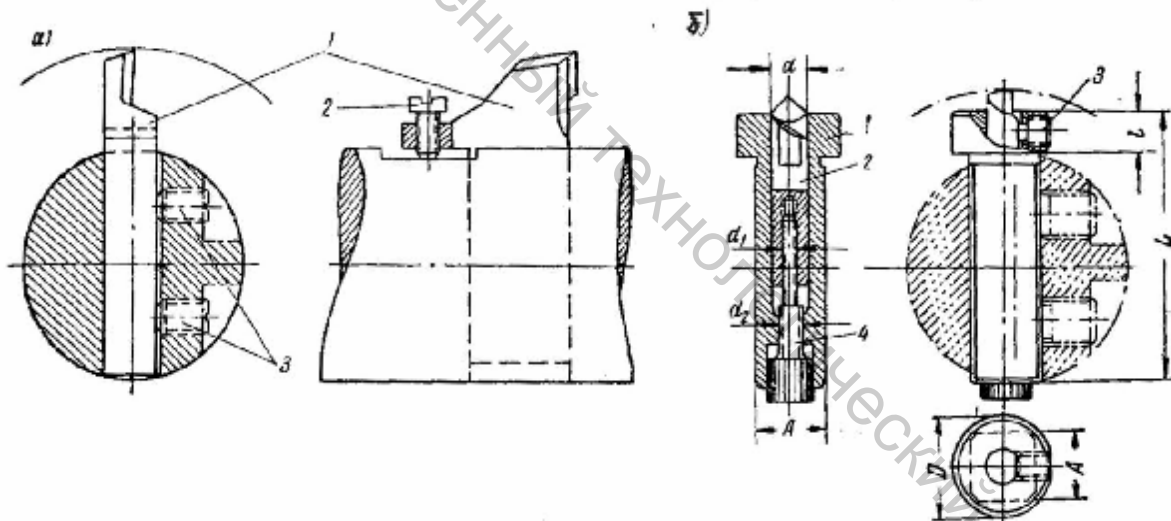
Анилажный резец (а) и однорезцовый блок с микрометрической регулировкой (б)
